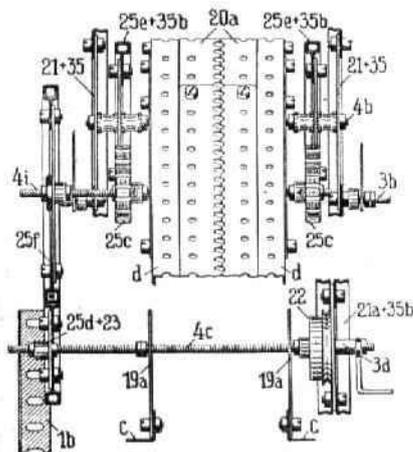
d ist eine Ansicht des Getriebes. Diese Abbildung gibt auch zugleich die Befestigung der Zahnräder und Schwingräder auf den verschiedenen Wellen wieder.
